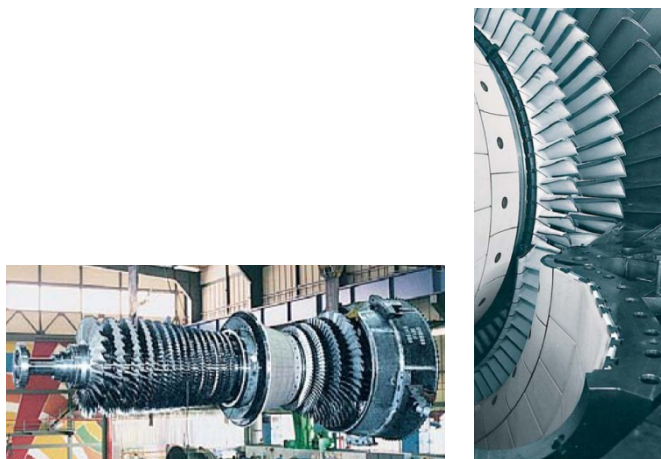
Rotor und Turbinenbeschaukelung der Siemens SGT5-4000F [10]
